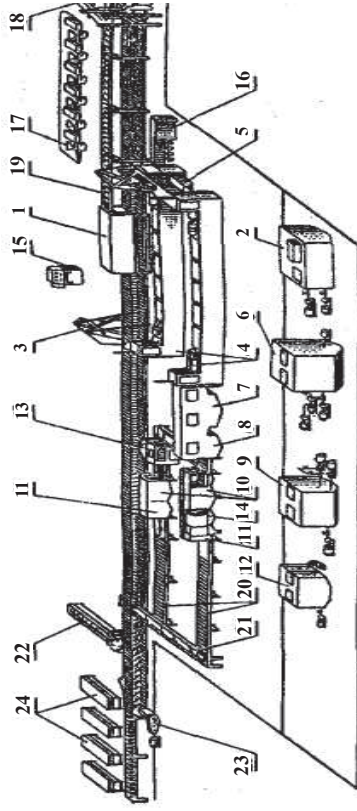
Поточная линия очистки деталей и сборочных единиц двигателей:
